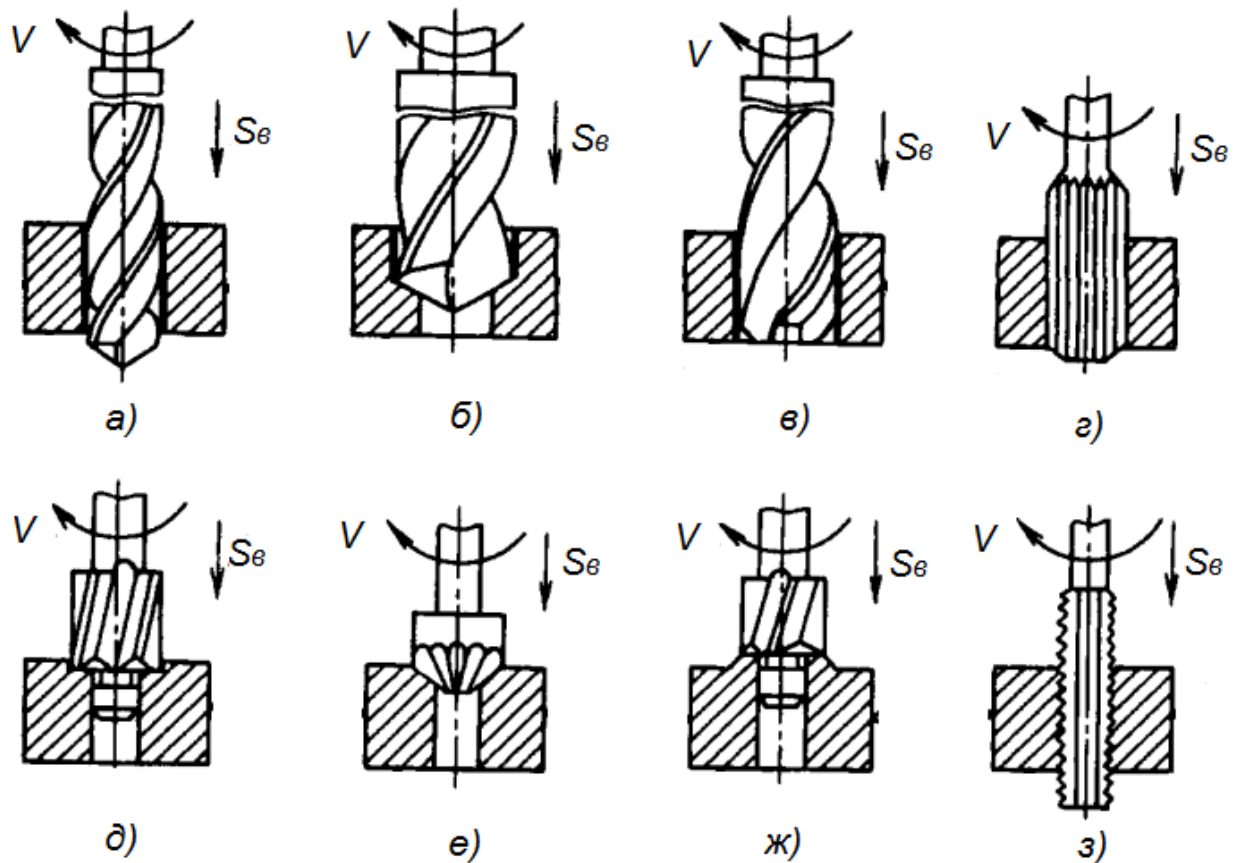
2. Схемы обработки поверхностей на сверлильных станках:
